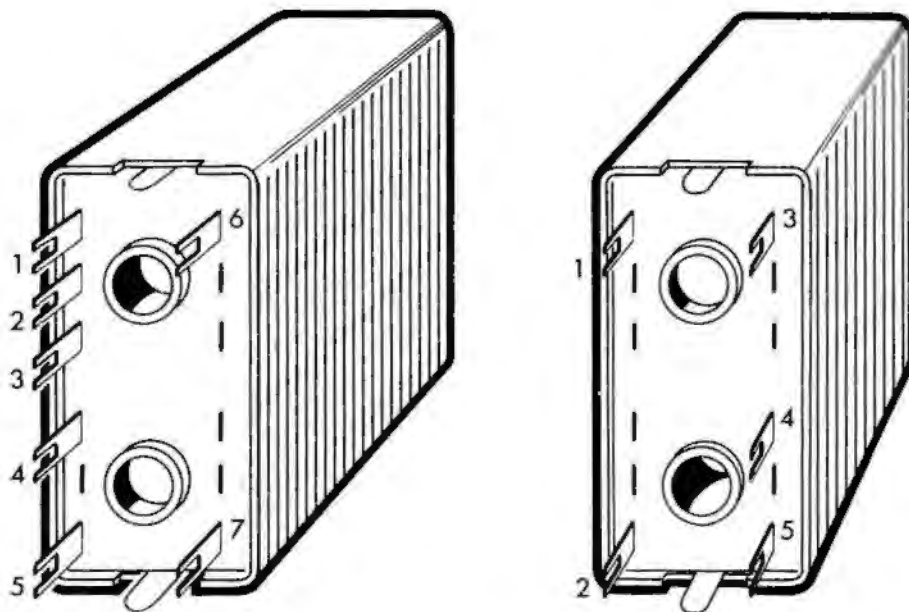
La soldadura en los terminales de los transformadores de F.I. debe hacerla rápidamente, sin obligar a éstos por una excesiva presión del soldador.
